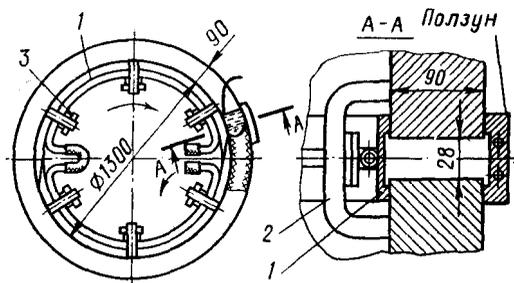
Кольцевой стык, собранный под электрошлаковую сварку
